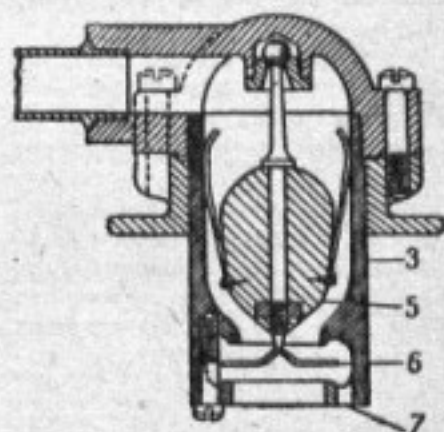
Поперечный разрез маятникового клапана пневматической рессоры
